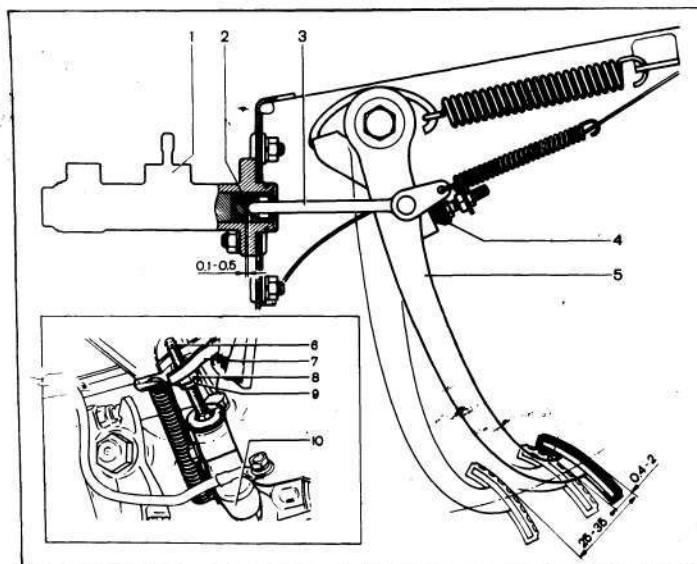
Регулировка привода выключения сцепления: 1 — главный цилиндр сцепления; 2 — поршень толкателя; 3 — толкатель; 4 — ограничитель хода педали; 5 — педаль сцепления; 6 — толкатель рабочего цилиндра; 7 — вилка выключения сцепления; 8 — гайка; 9 — контргайка; 10 — рабочий цилиндр
